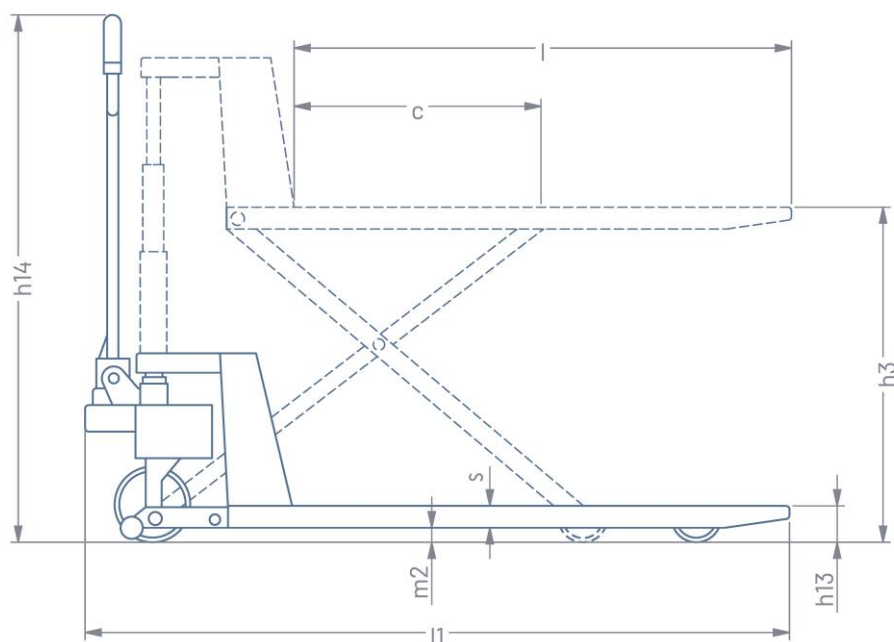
ZAC-C Seitenansicht mit Kürzeln
